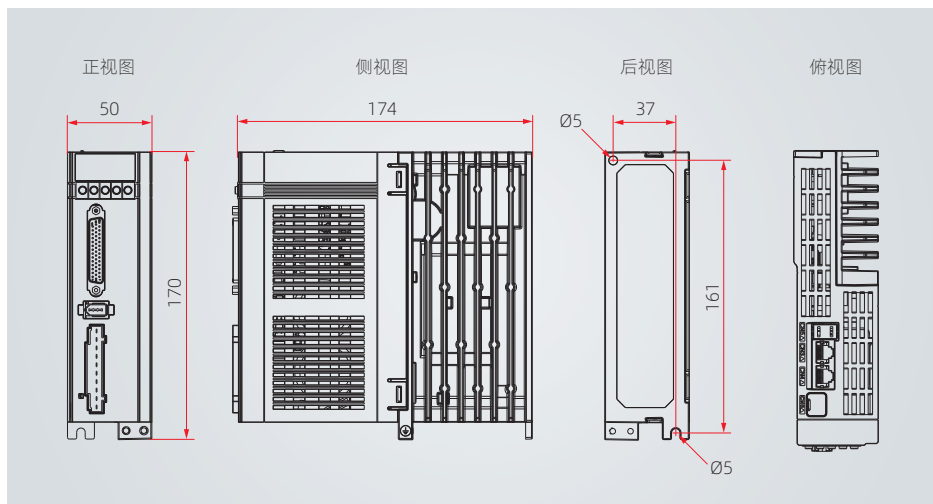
驱动器 (SIZE B) 安装尺寸示意图 (单位: mm)
